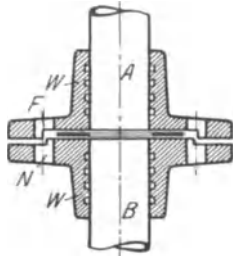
Aufgedrillte Flanschen mit Federn und Nut.
